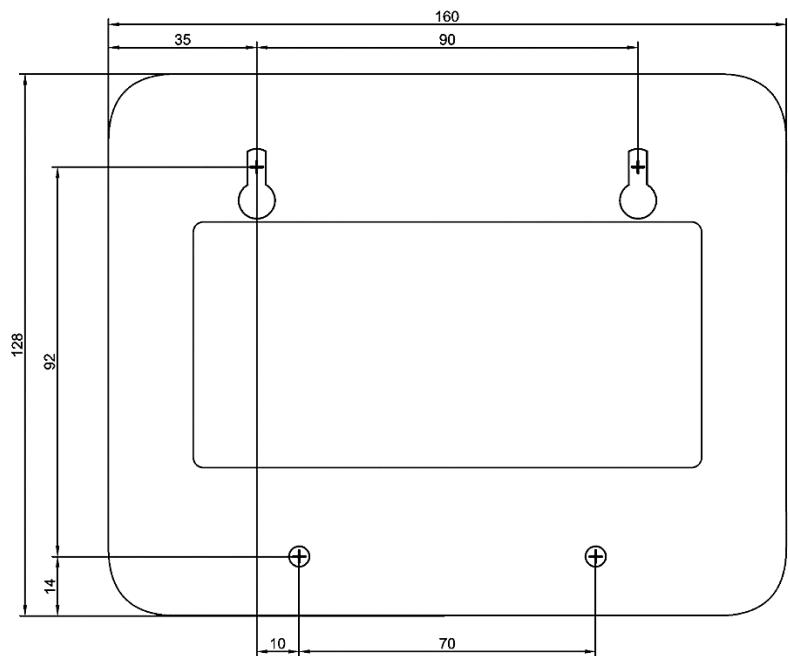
Разметка отверстий для крепления прибора КОП-02.4 (вид со стороны передней панели)
